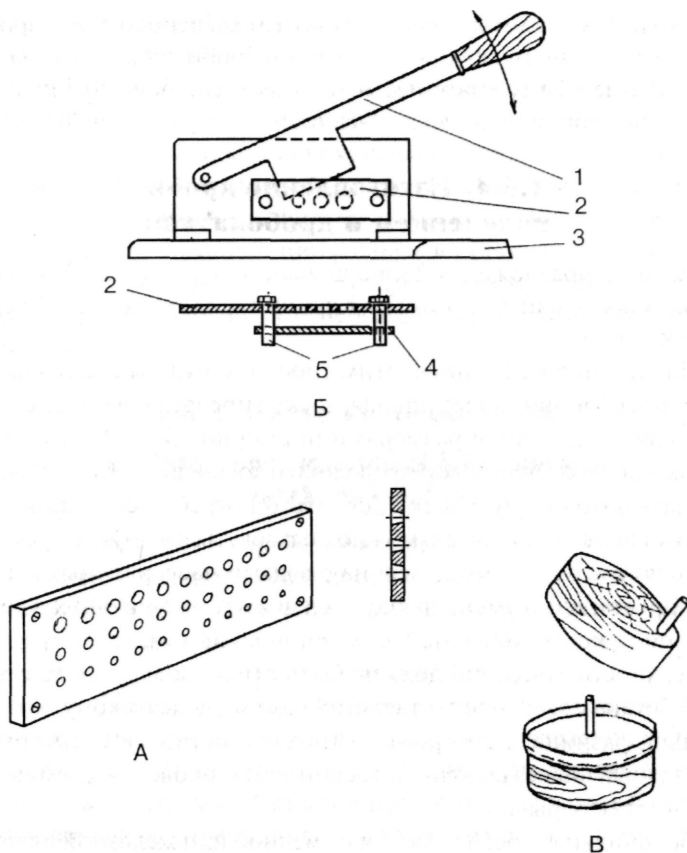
Приспособления для изготовления дрови волочением и дробокаткой:
